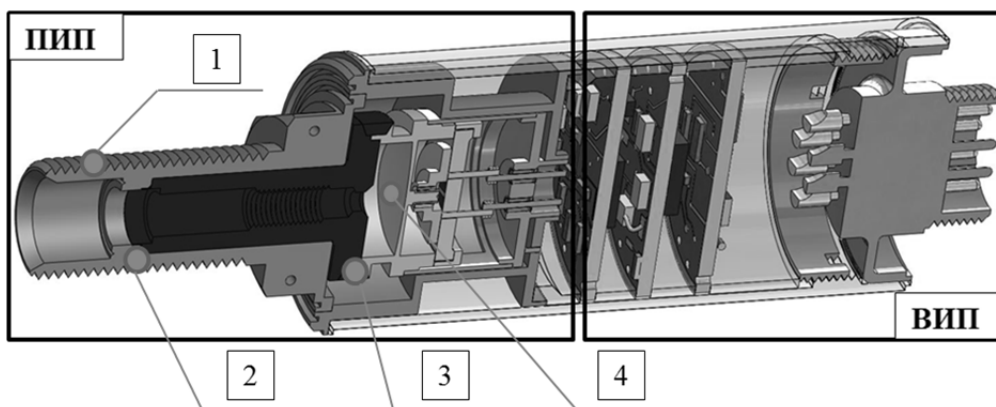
Общий вид датчика с цифровым выходом: 1 – резьбовое штуцерное соединение датчика с гнездом присоединительного затвора; 2 – сварное соединение гайки с наконечником и штуцером (сварной шов); 3 – сварное соединение мембраны с штуцером (сварной шов); 4 – мембрана
